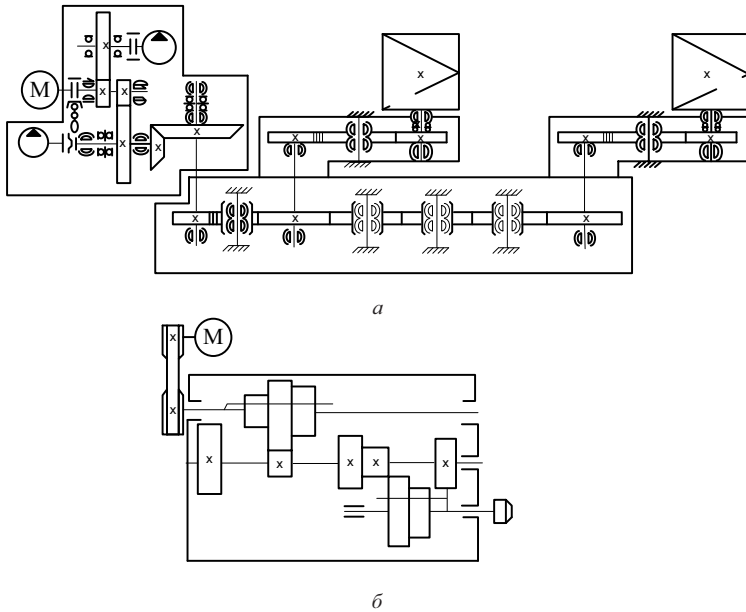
Приводы главного движения: а – исполнительного органа редукторов комбайна 1К101; б – коробки скоростей на  $z = 6$
